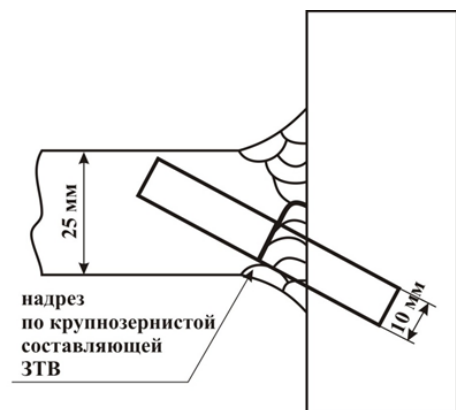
Схема изготовления образцов из заготовок
